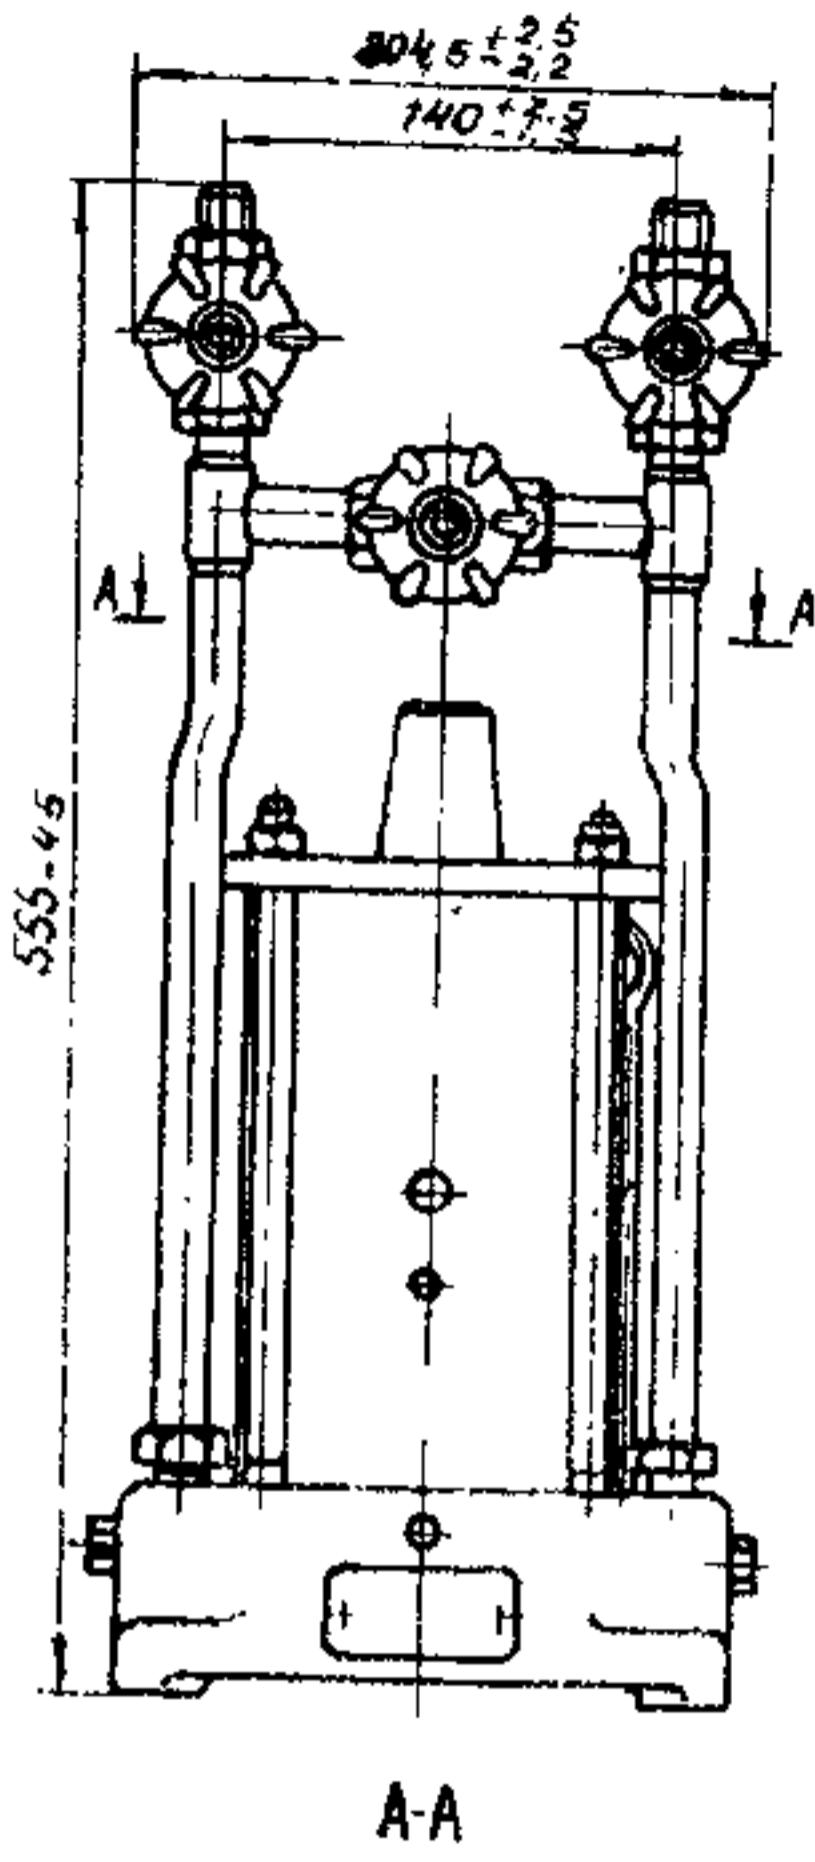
Габаритный чертеж с монтажными и присоединительными размерами.
